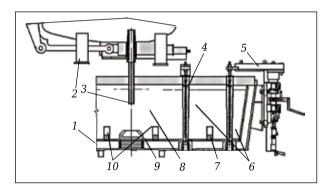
Компоновка ПК четырехручьевой МНЛЗ: 1- ПК; 2- сталеразливочный ковш; 3- труба; 4- стопор; 5- механизм стопора; 6- разливочные камеры ПК; 7- порог разливочной камеры; 8- приемная камера ковша; 9- донный металлоприемник; 10- пороги приемной камеры
